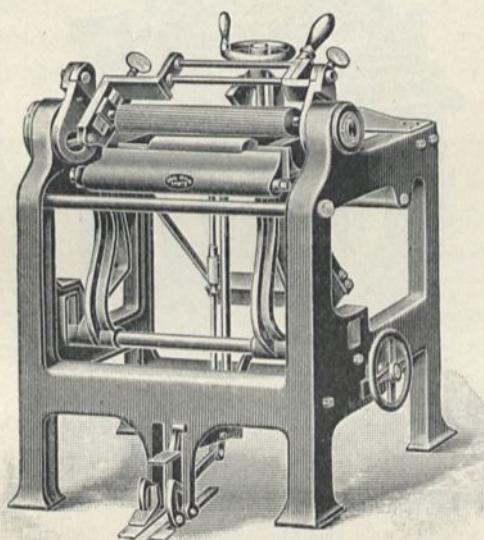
Abpreßmaschine von Diez & Lüfting, Leipzig.
